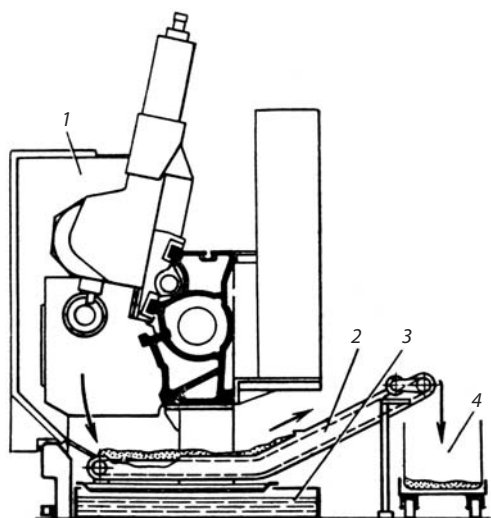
Схема удаления стружки на токарном станке с ЧПУ:
